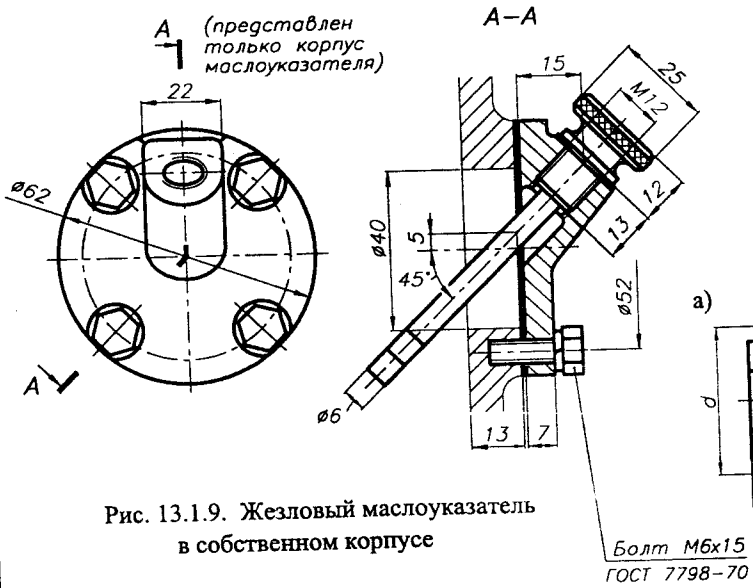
Жезловый маслоуказатель в собственном корпусе
